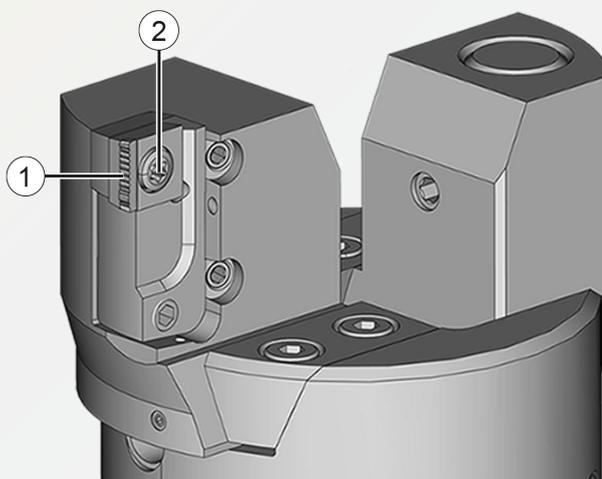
Desserrage de la vis de serrage sur la plaquette d'abrasion
